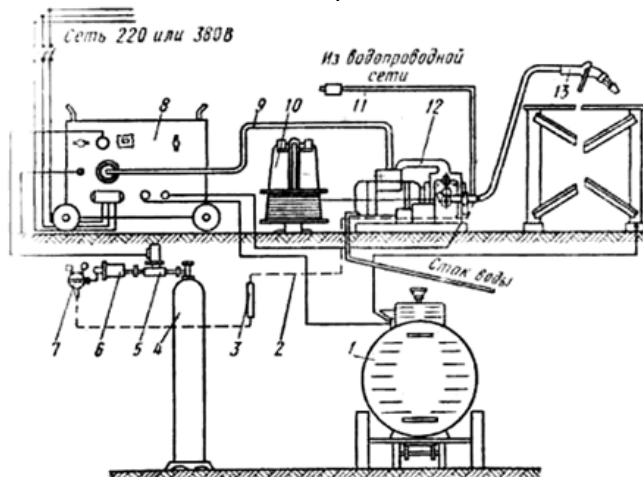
Схема поста А-537 для полуавтоматической сварки в углекислом газе проволокой диаметром 1,6 — 2 мм: 1 — источник сварочного тока; 2 — резиновая трубка (шланг) для подвода углекислого газа в горелку; 3 — расходомер газа; 4 — баллон с жидкой углекислотой; 5 — подогреватель газа; 6 — предредукторный осушитель; 7 — газовый редуктор; 8 — шкаф управления; 9 — спецпровод с проводами управления; 10 — кассета с проволокой; 11 — резиновая трубка (шланг) для подвода охлаждающей воды; 12 — подающий механизм полуавтомата; 13 — газоплазменная горелка с принудительным охлаждением водой
